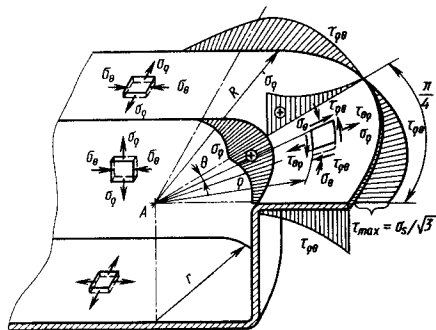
Распределение напряжений в части фланца на угловых скруглениях при вытяжке коробчатой детали
